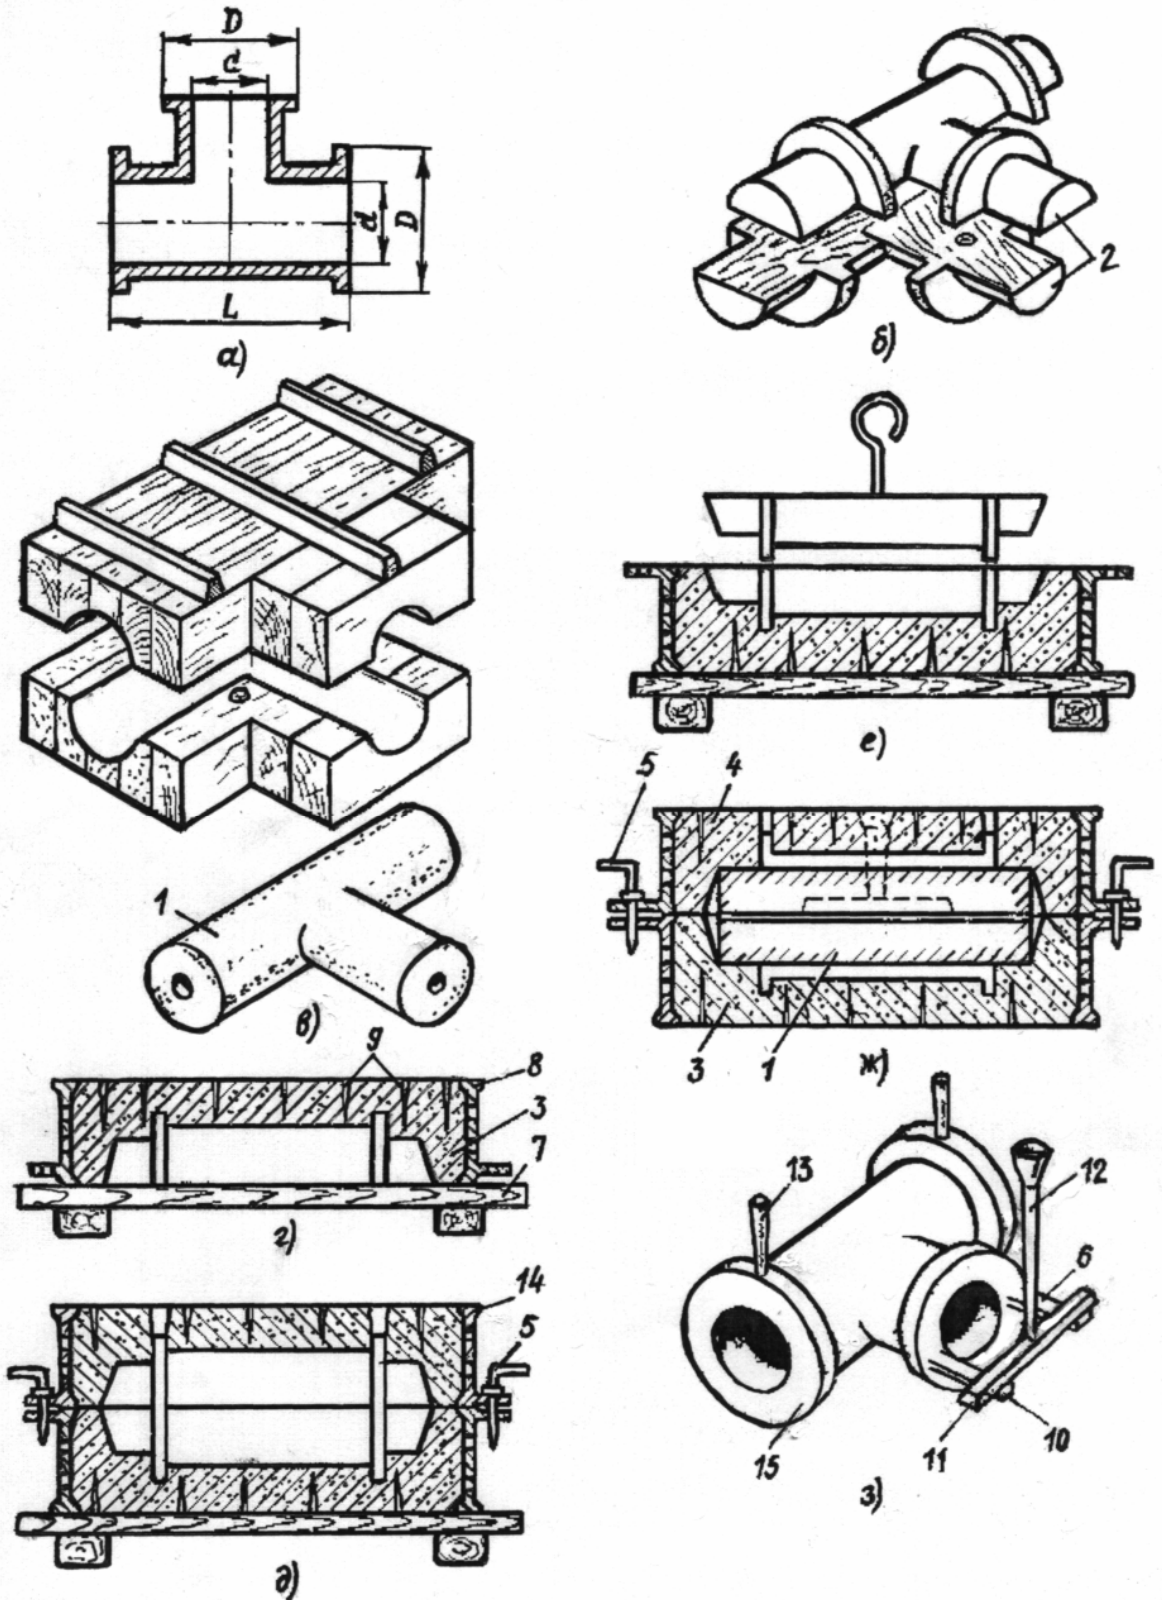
Изготовление разовой формы для отливки «тройник»
